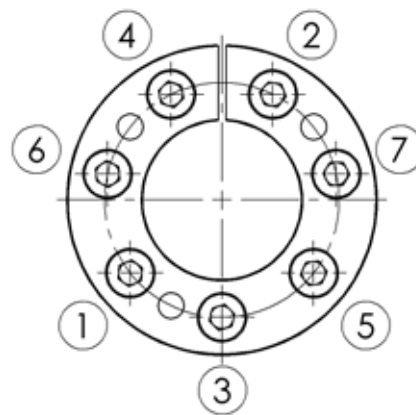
Sequenz Aufschraubung Schrauben auf Verbinder Zahnräder.
